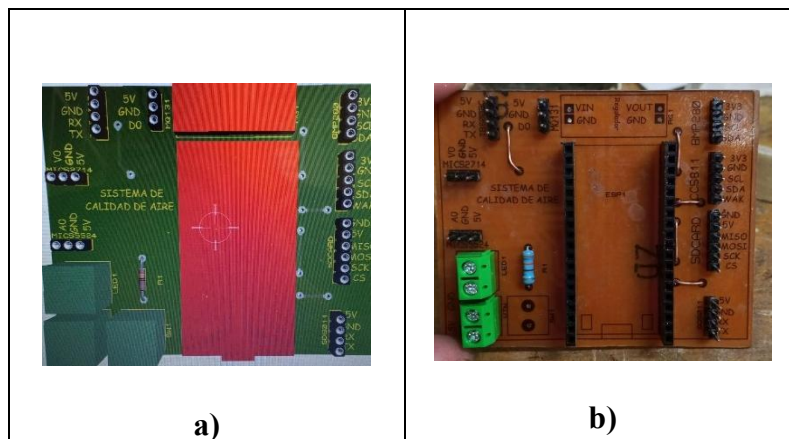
a) Diseño electrónico del sistema sensorizado, b) Placa PCB impresa
